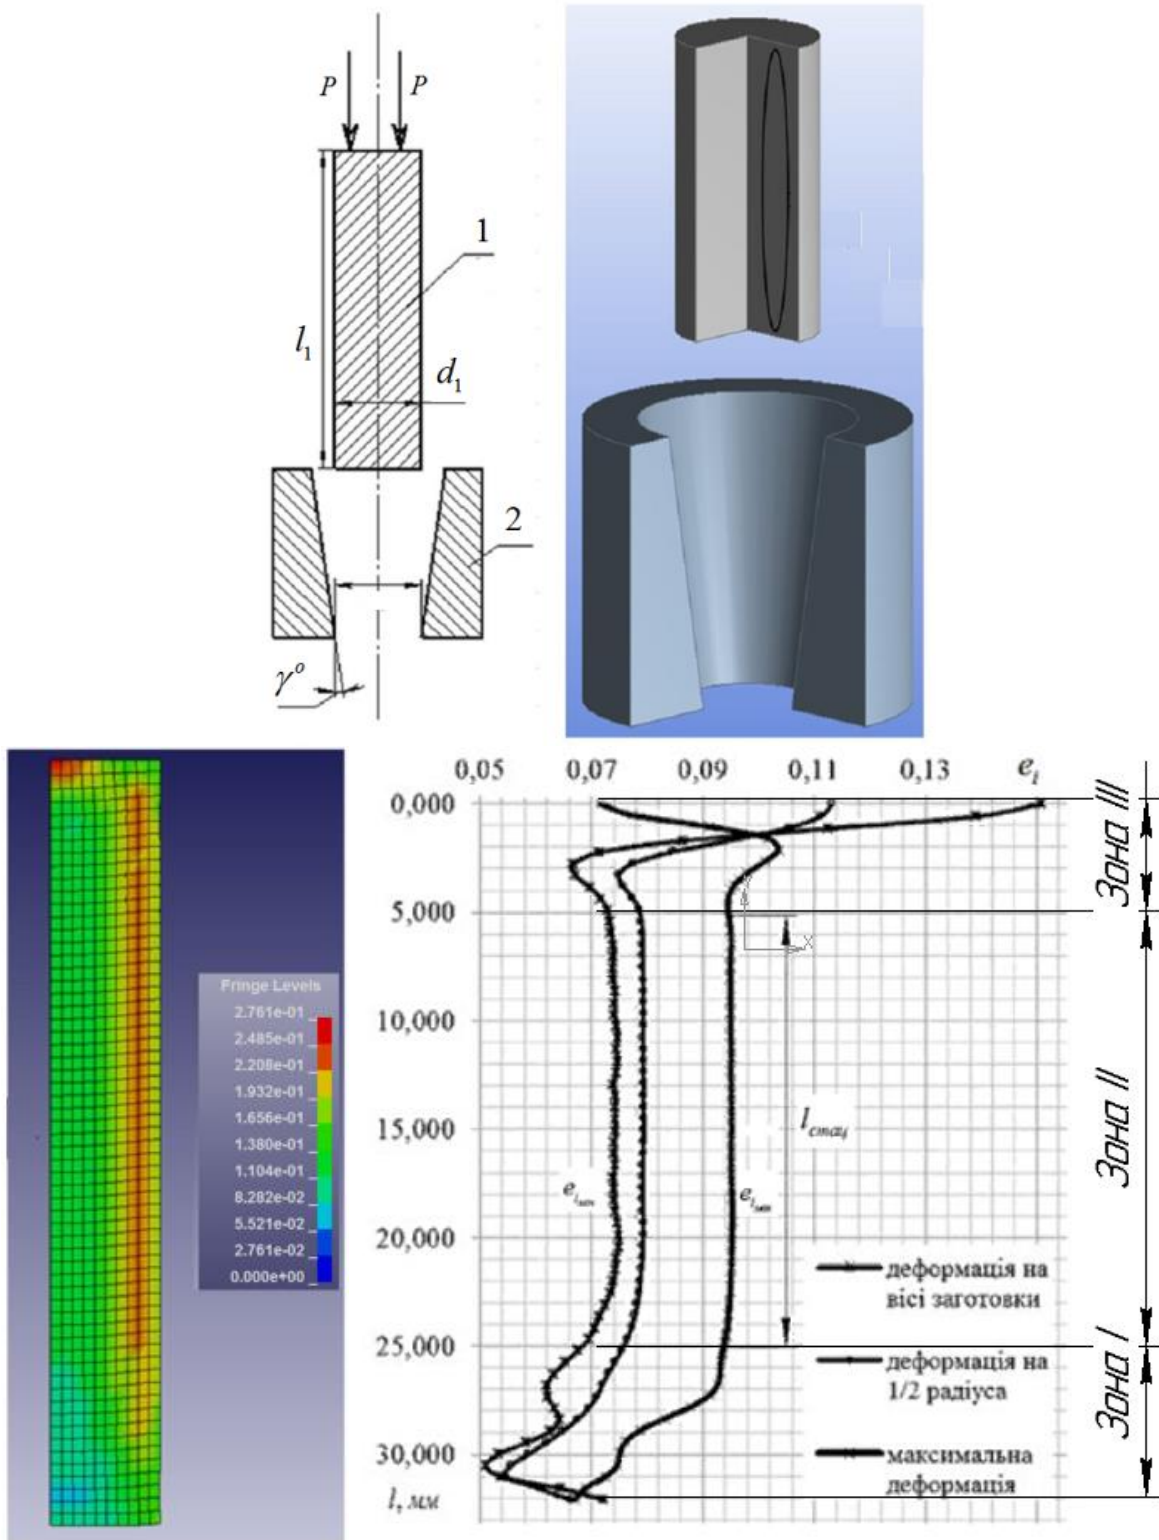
Редукування заготовки (1 – заготовка, 2 - матриця)
